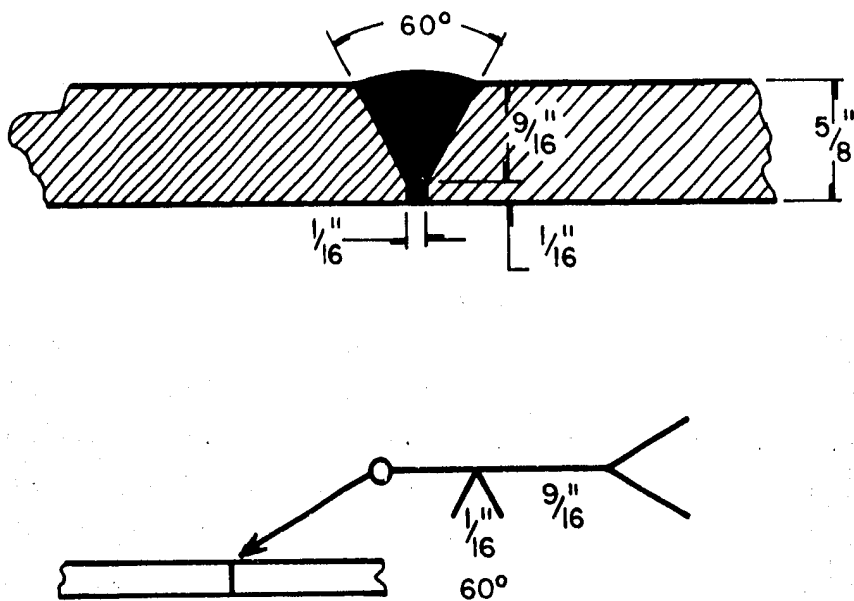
DETALLE DE SOLDADURA Y SIMBOLOGIA ASOCIADA.
